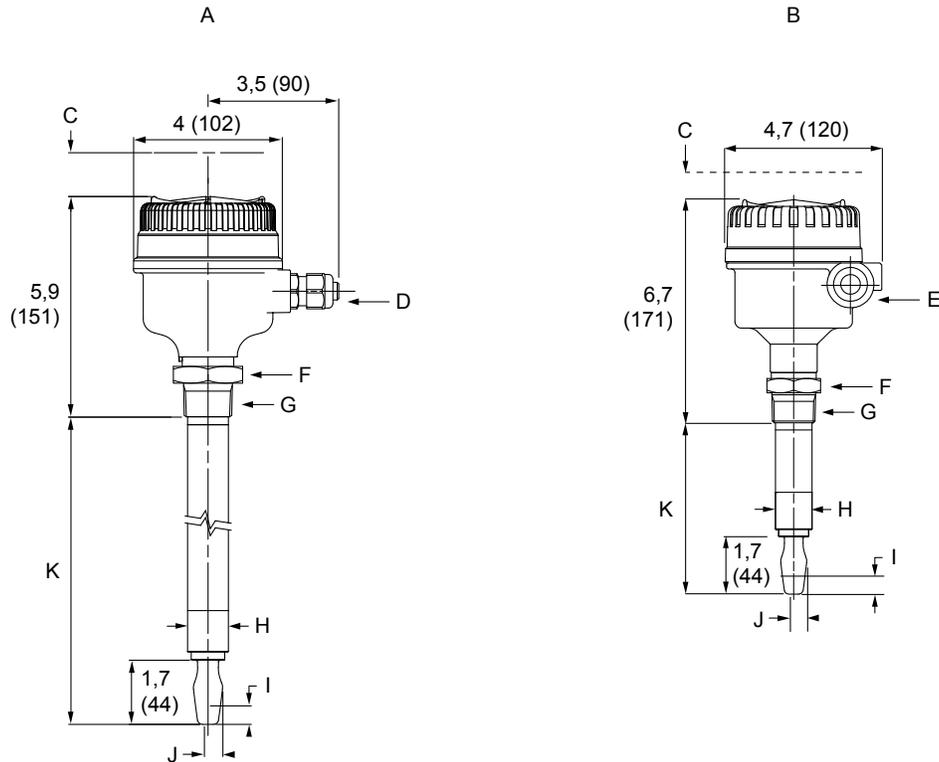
3/4 und 1 in. Gewindemontage (Standardlänge)
